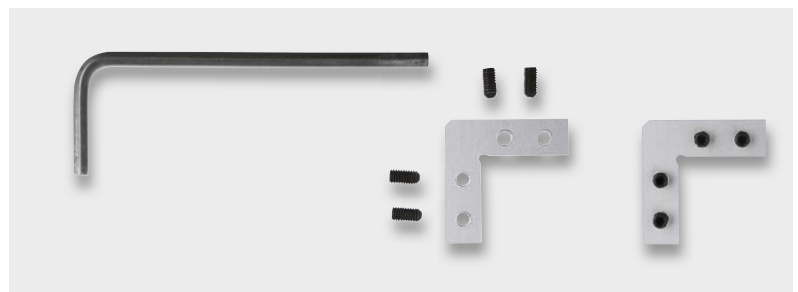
Die Alu-Winkel werden mit Gewindestiften am Rahmen befestigt.
